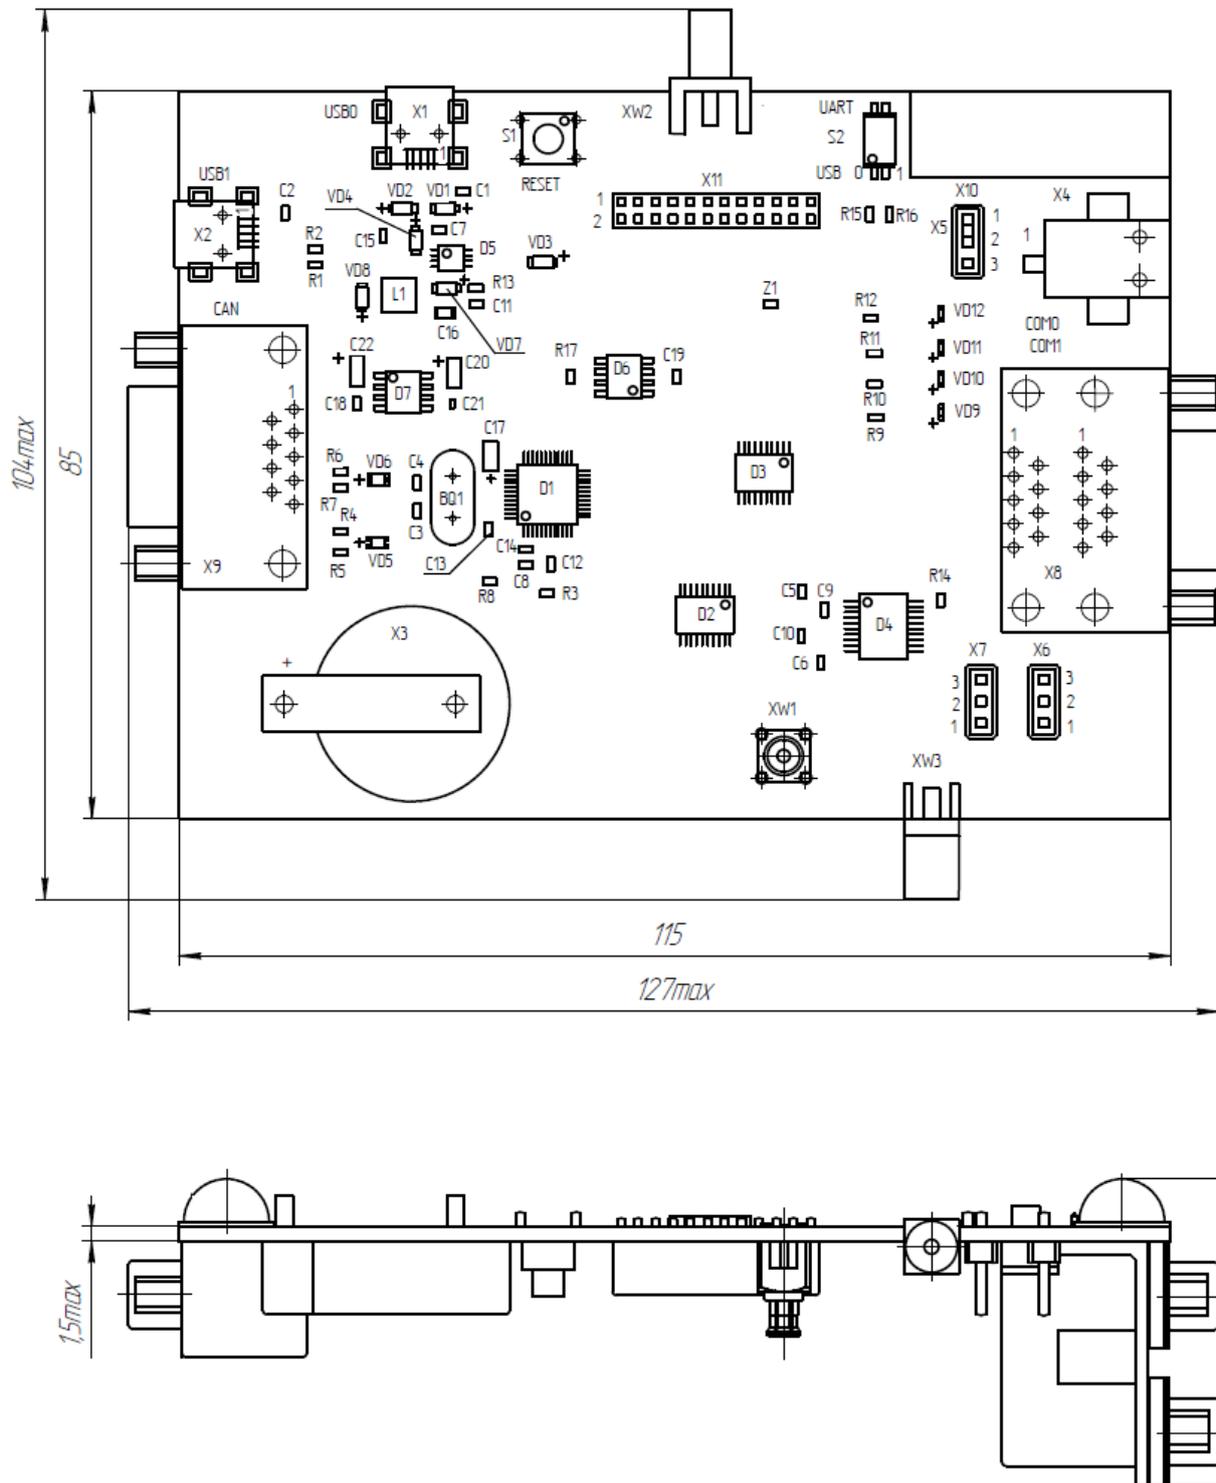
Габаритный чертеж средства отладочного ЦВИЯ.468364.164
